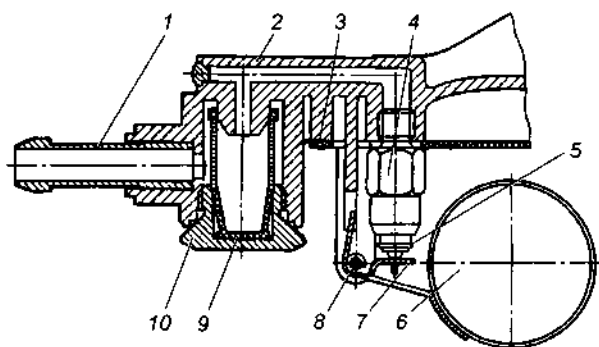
Поплавковый механизм карбюраторов ДААЗ: 1 — входной штуцер; 2 — крышка карбюратора; 3 — прокладка; 4 — корпус клапана с седлом; 5 — игольчатый клапан; 6 — поплавок; 7 — язычок; 8 — ось; 9 — сетчатый фильтр; 10 — резьбовой держатель фильтра
